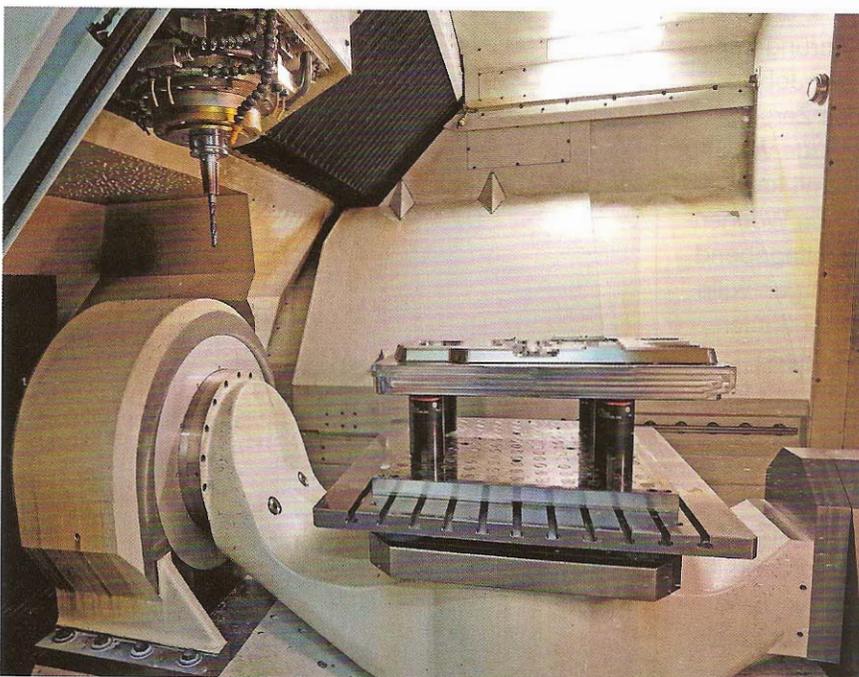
Im internen Werkzeugwechsler ist genügend Platz für Werkzeuge mit Längen bis zu 380 mm
